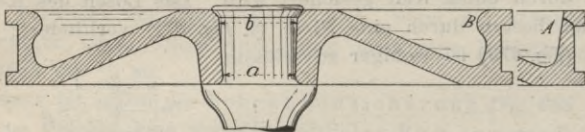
682. Kolben für 3000 kg-Dampfhammer.
